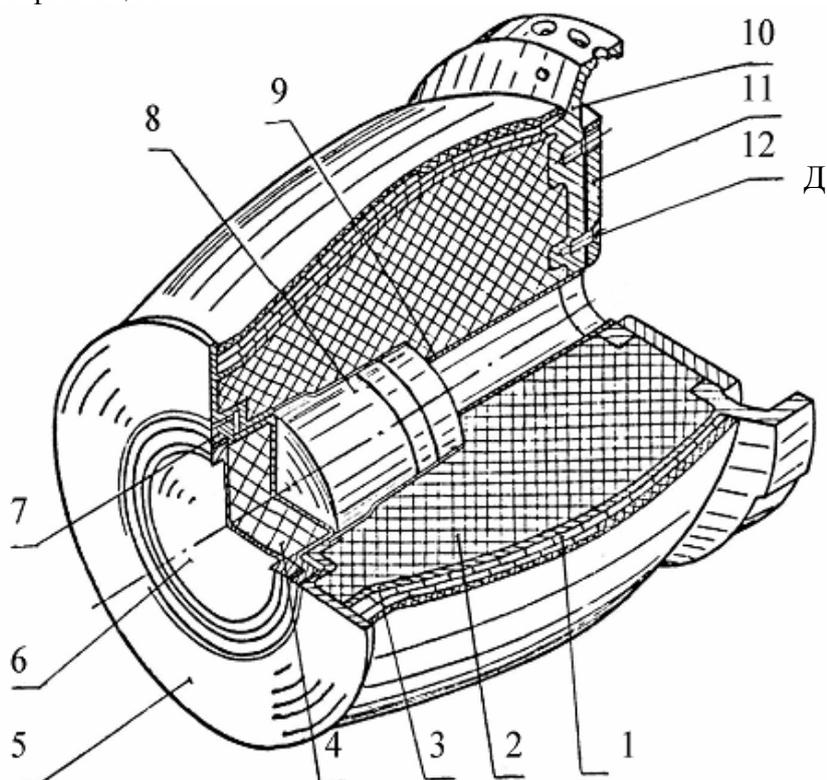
Боевая часть: 1 – поражающие элементы; 2 – заряд ВВ; 3, 9 – оболочка; 4 – шашка; 5, 10 – фланец; 6, 11 – крышка; 7 – гайка; 8 – ПИМ; 12 – винт
